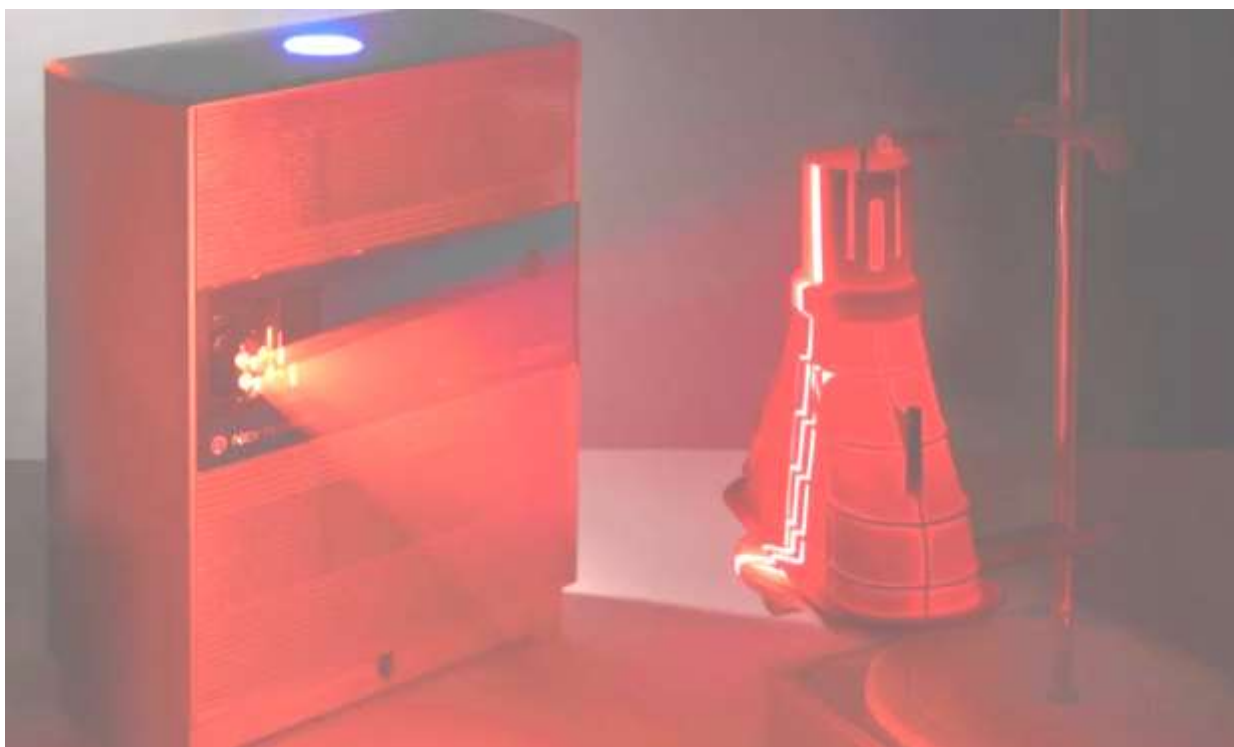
3D-сканер є найпоширенішими пристроями захоплення для реверсивної інженерії.
